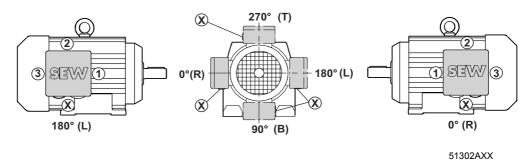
Lage des Klemmenkastens und der Kabeleinführung
